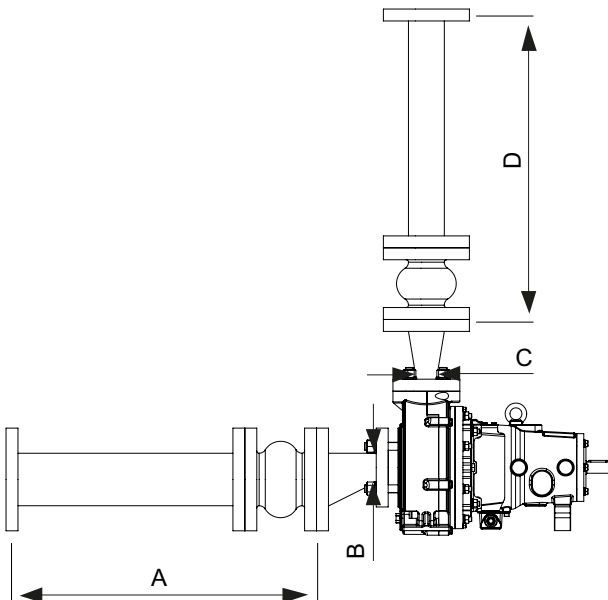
Gerade Rohrleitungslängen vor und nach der Pumpe (empfohlen)
